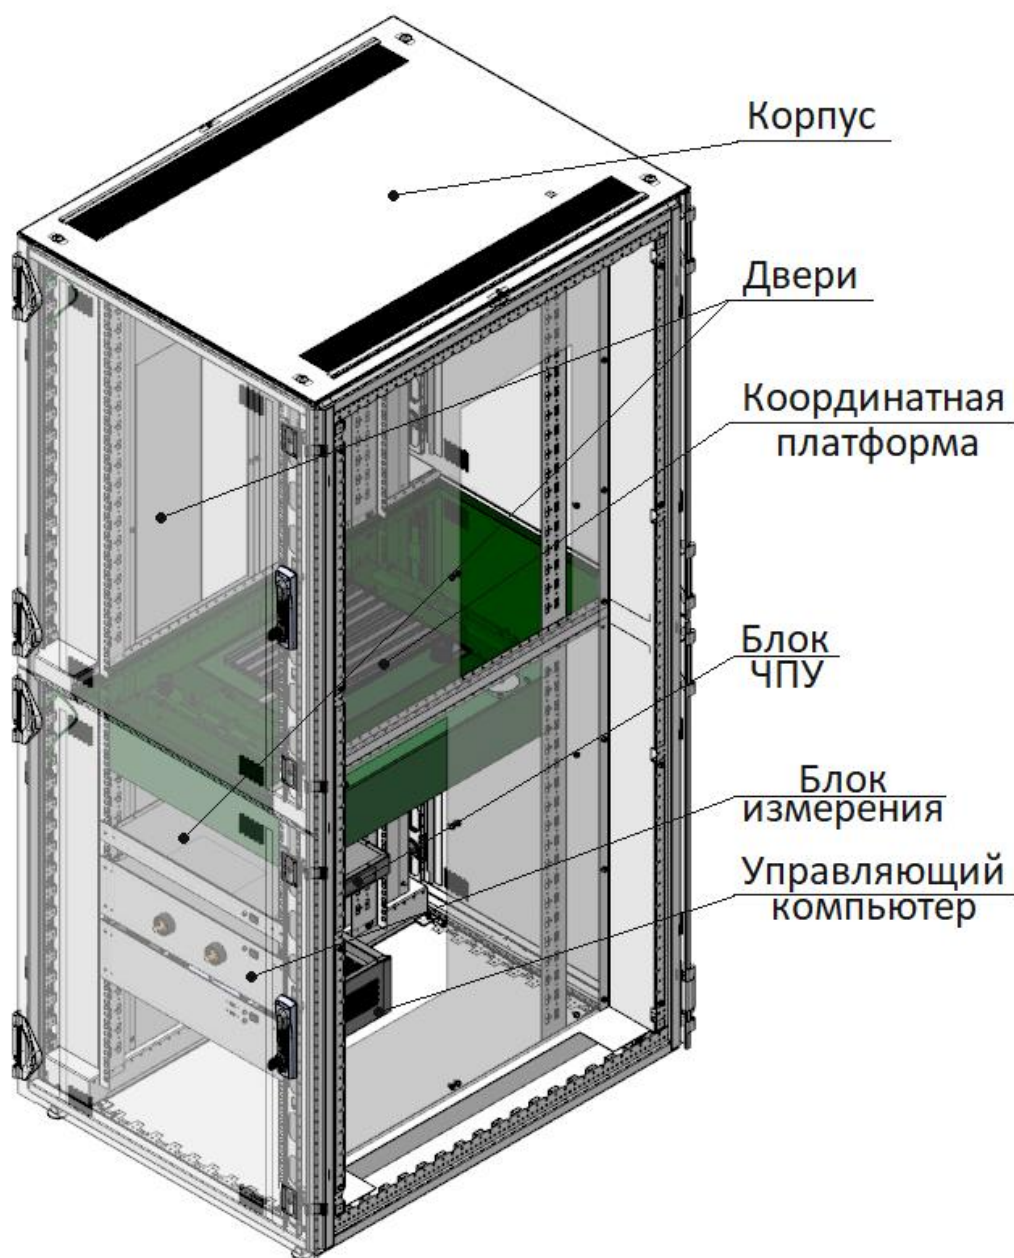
Модель автоматизированной установки для исследования процессов дуговой сварки и наплавки
